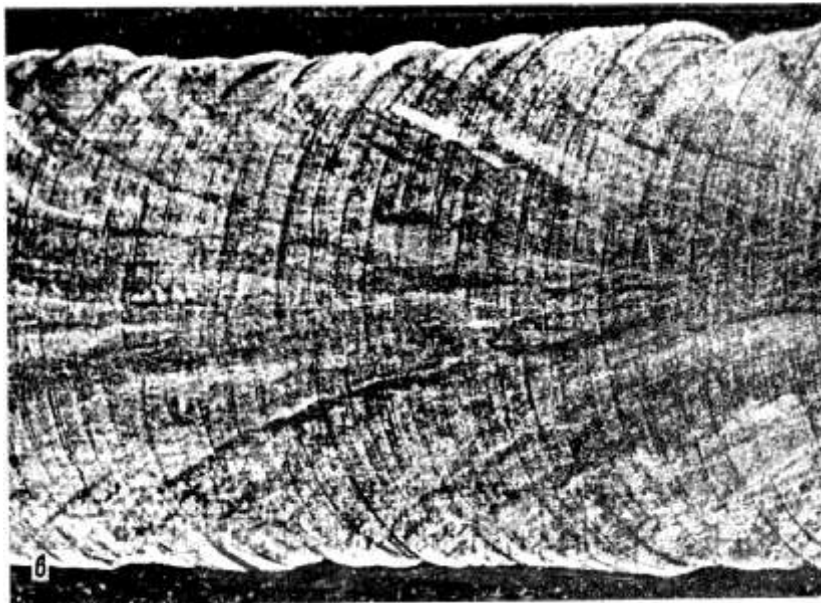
Внешний вид поверхности сварного шва с чешуйчатым строением $\times 5$
